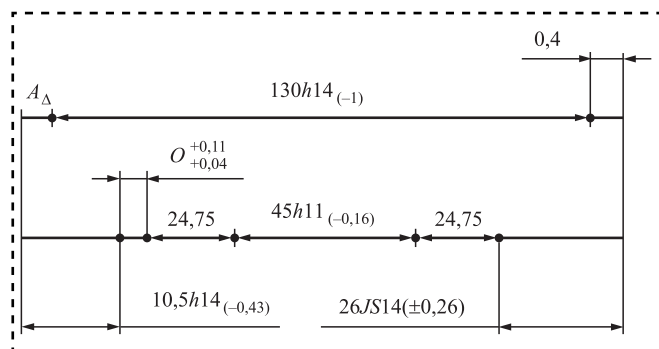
Размерная цепь выходного вала редуктора 4МЦ2С-80
